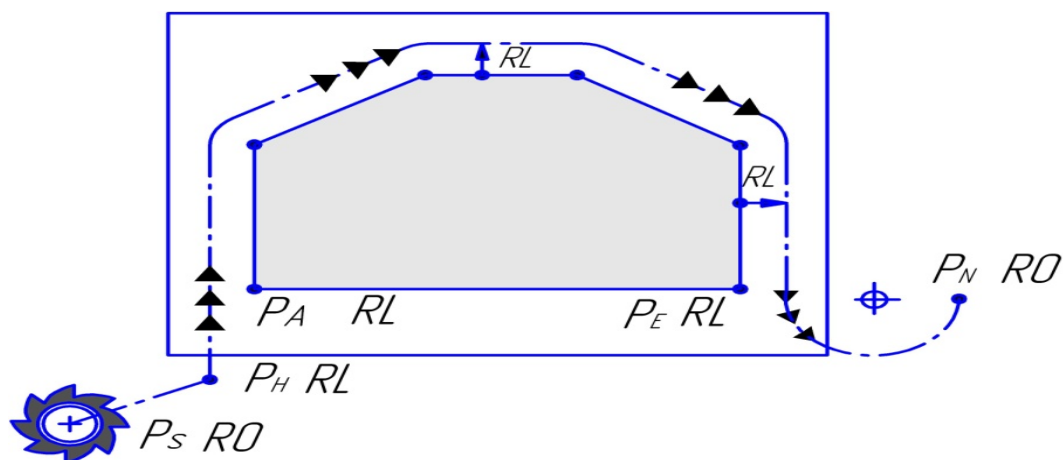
Подвод и отвод инструмента при обработке контура заготовки
